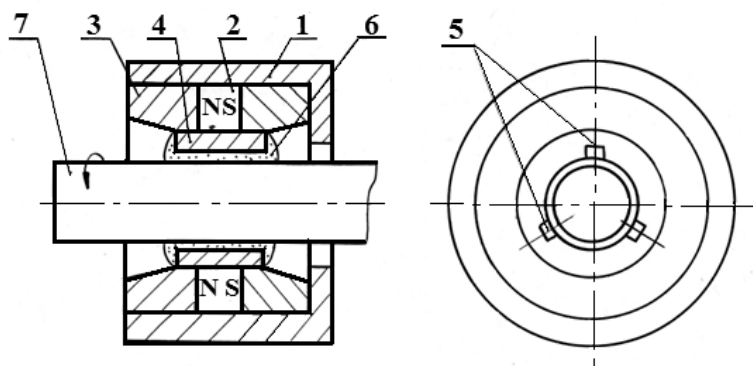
Принципиальная схема магнитожидкостного подшипника
